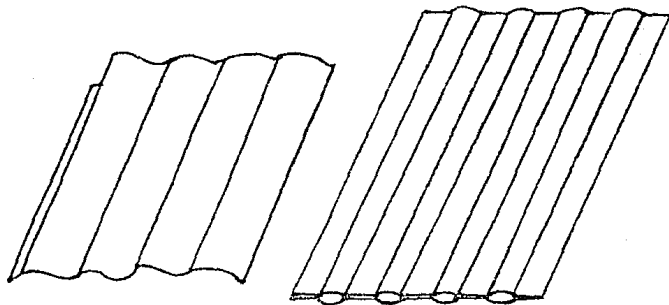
Lámina ondulada soldada a una placa plana
